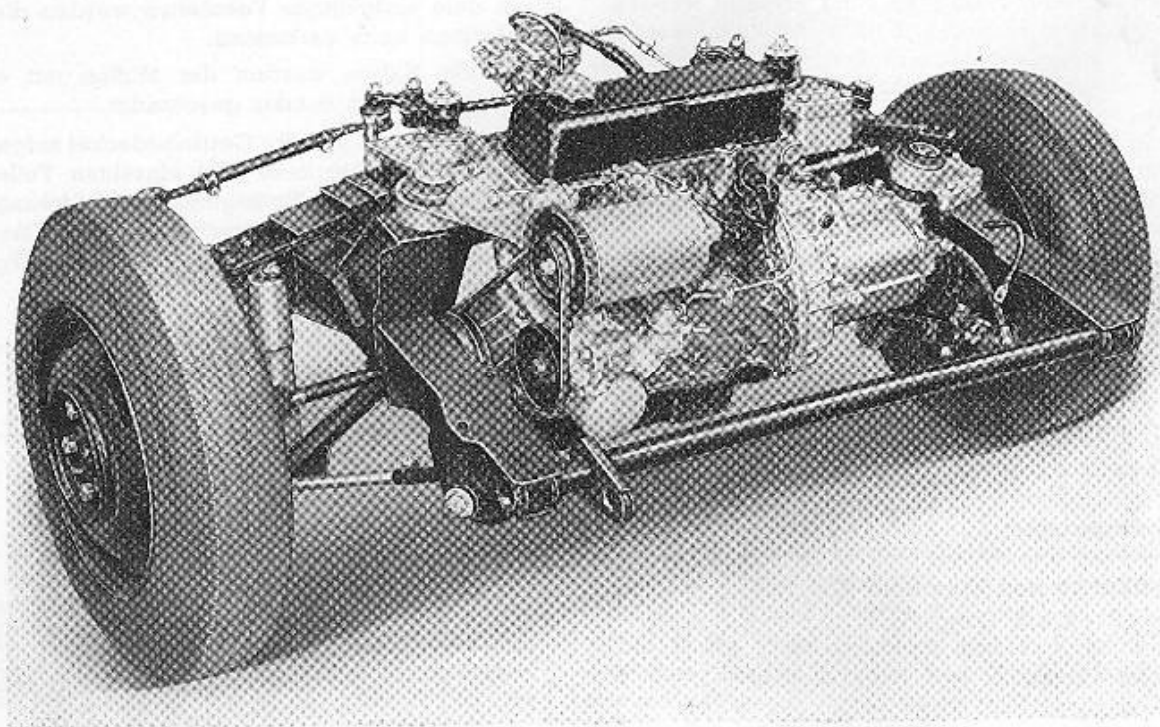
Rechte Seitenansicht der vorderen Radaufhängung und Motoraufhängung.
